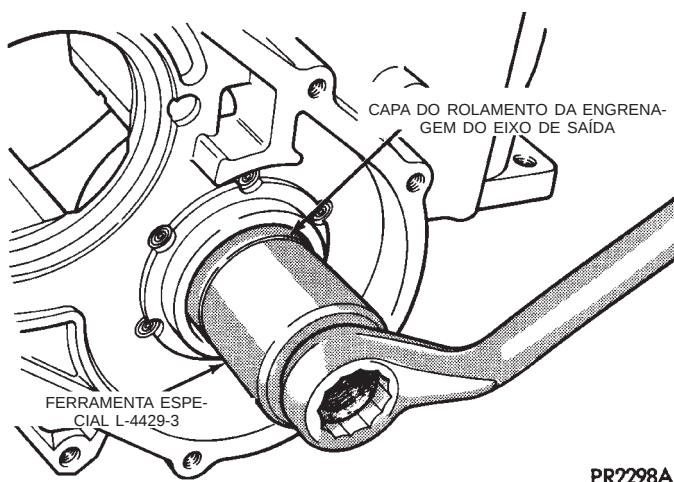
Instalação da Capa de Rolamento da Engrenagem do Eixo de Saída
